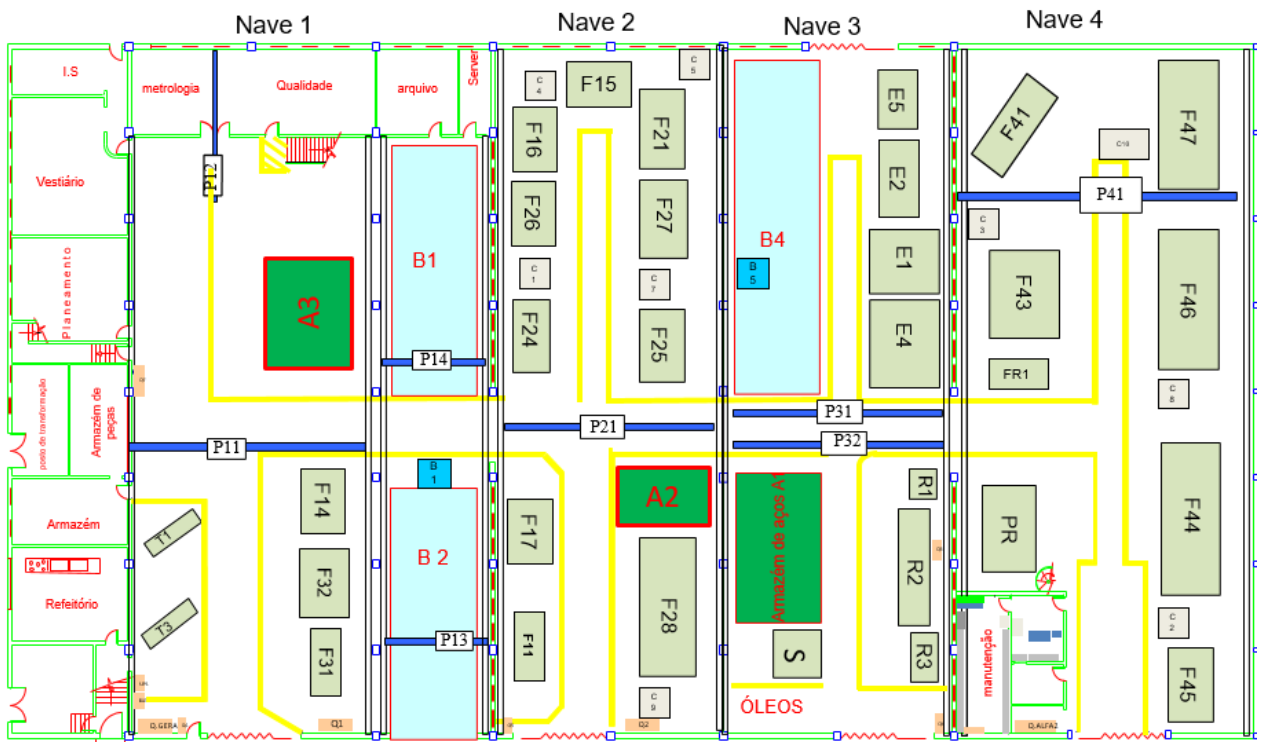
Proposta de novo Layout - Layout 2- (escala 1:200)
